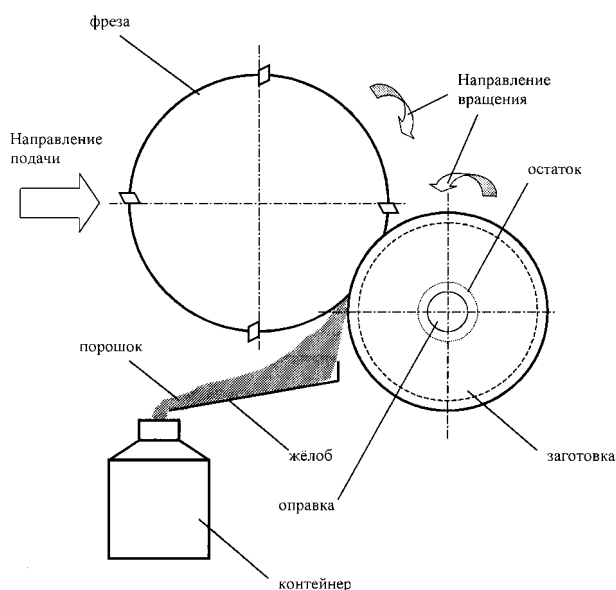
Схема получения металлических порошков фрезерованием
